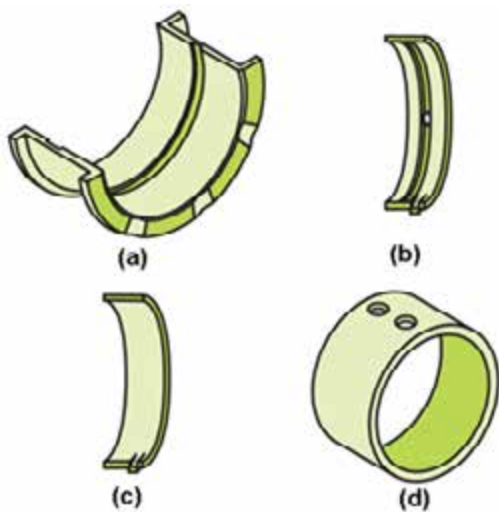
Типичные подшипники, применяемые в современных автомобильных двигателях: (a) полу-корпусной упорный подшипник; (b) верхний вкладыш коренного подшипника; (c) нижний вкладыш коренного подшипника, или вкладыш шатунного подшипника; (d) полнотельный вкладыш подшипника распределительного вала; источник: *Pearson Education, Inc.
